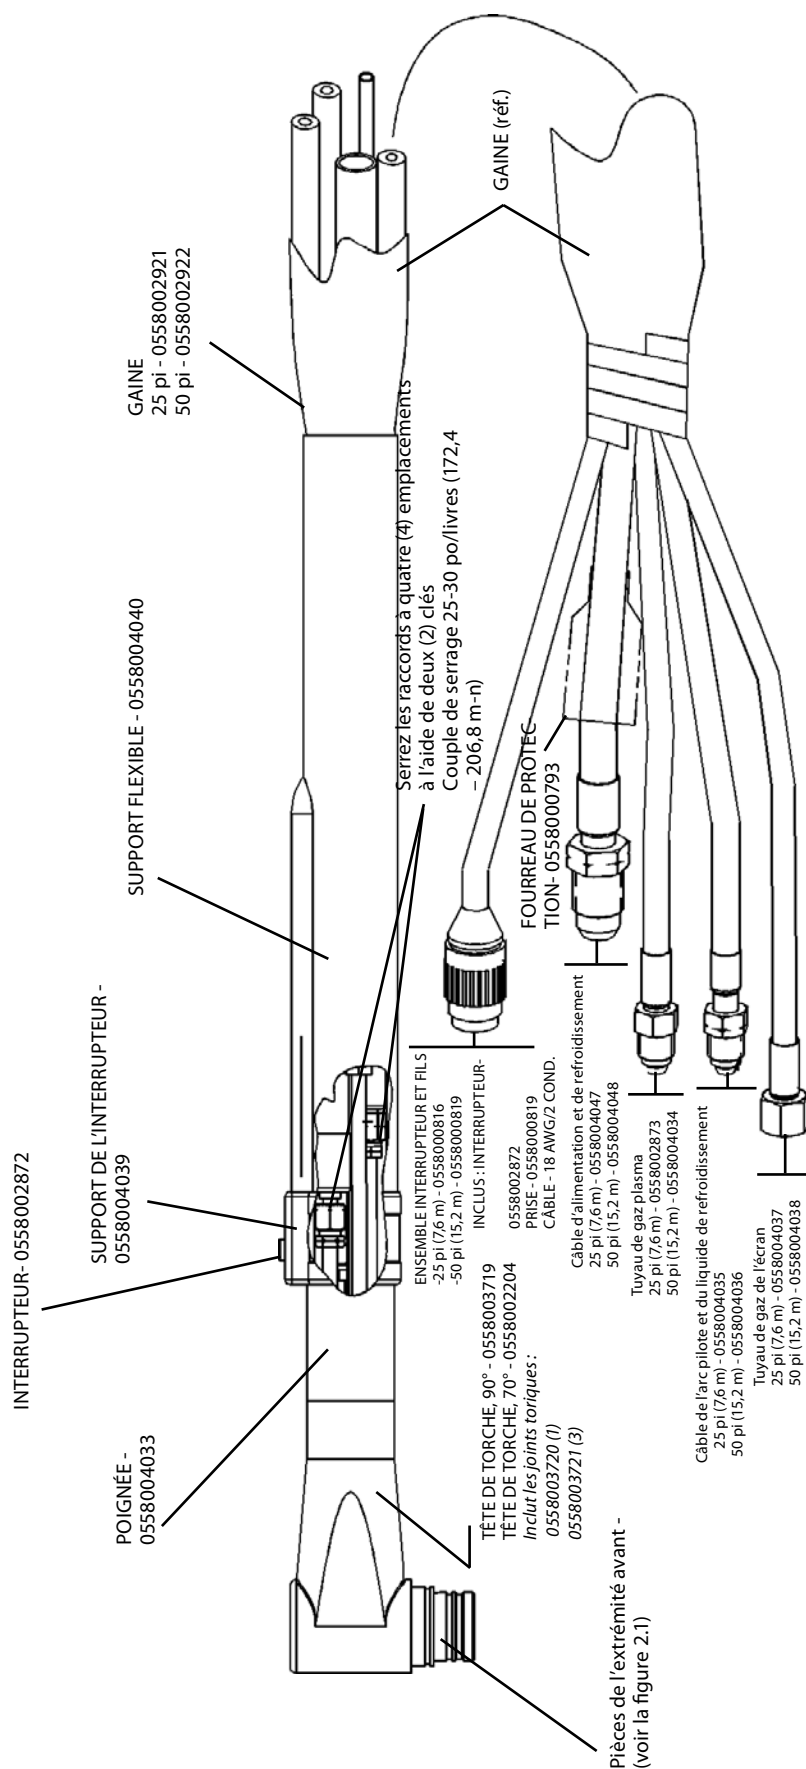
Pièces de rechange - ensemble de la torche PT-26
